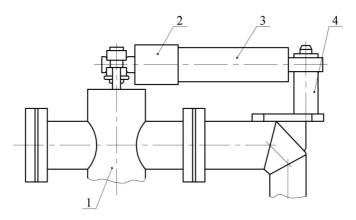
Механизм перекрытия вентиля: 1 – вентиль; 2 – ручка; 3 – гидроцилиндр; 4 – кронштейн
